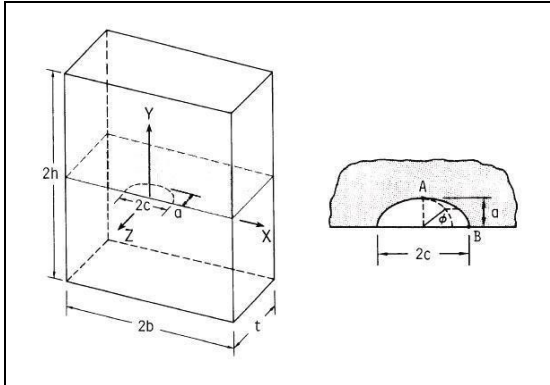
Fisura superficial en placas planas soldadas a tope: X - orientación de la junta soldada (el detalle de la geometría de la junta está indicado en esta Fig. 2); Y orientación de la tensión membranar, Pm; 2c - largo de la imperfección; a - profundidad de la imperfección proyectada en la dirección perpendicular a la tensión membranar, Pm; t = 12,7 mm, 2b = 2000 mm, 2h = 12000 mm.
